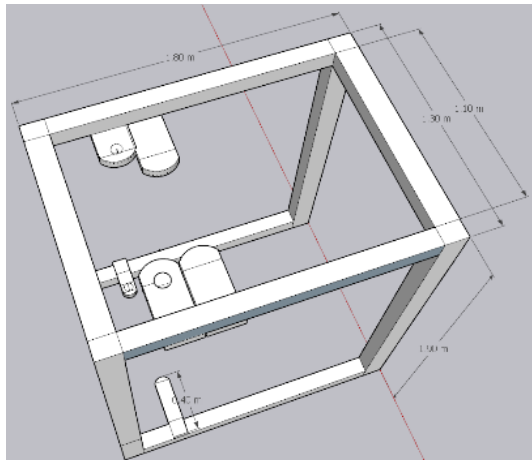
Vista superior de la Estructura principal de la cosechadora.
